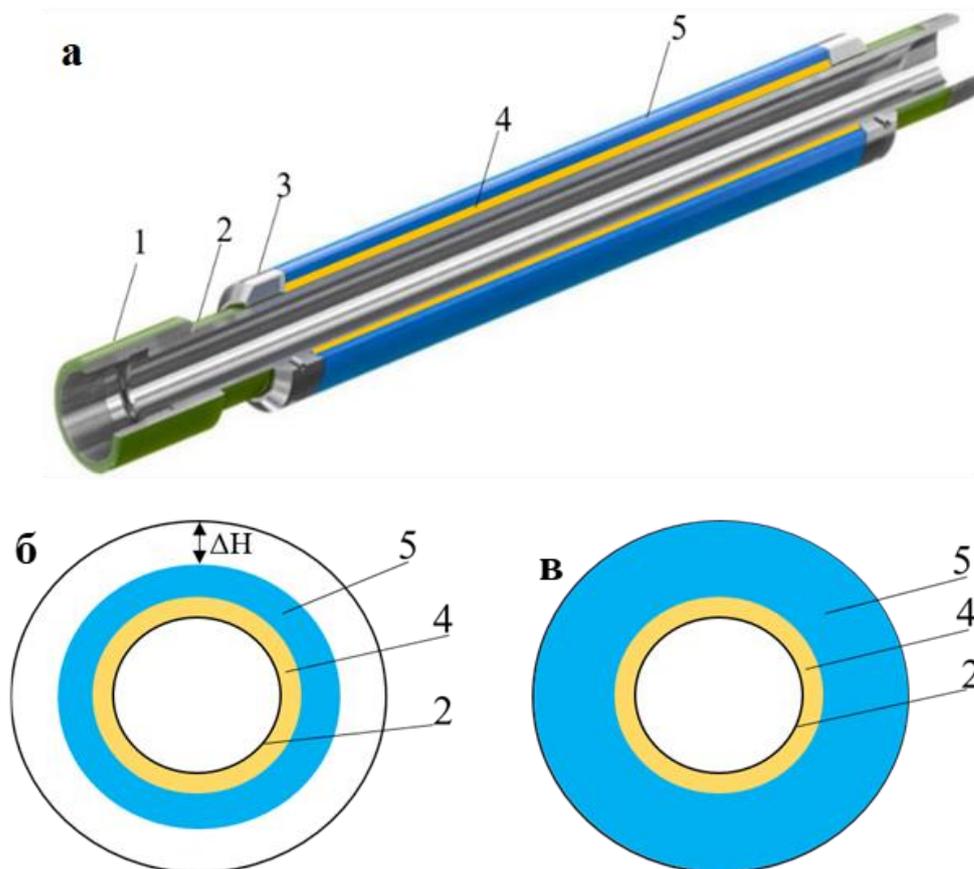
Конструкция двухслойного пакера (а): 1 – муфта; 2 – обсадная труба; 3 – противоэкструзионное защитное упорное кольцо; 4 – первый слой пакера; 5 – второй слой пакера; ΔH – зазор между стеной скважины и внешней поверхностью пакера, (б) схема набухания исходного двухслойного пакера до набухания и (в) после набухания
